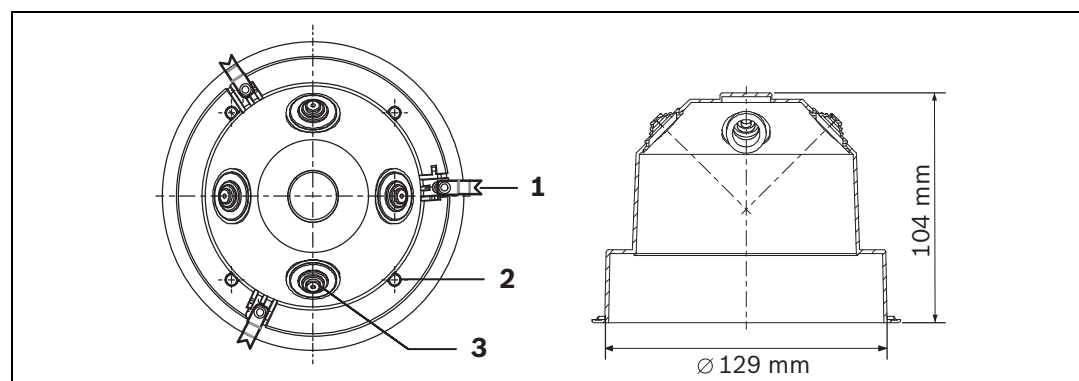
Vues en plan et de côté du boîtier arrière pour montage au plafond FAA-500-BB
